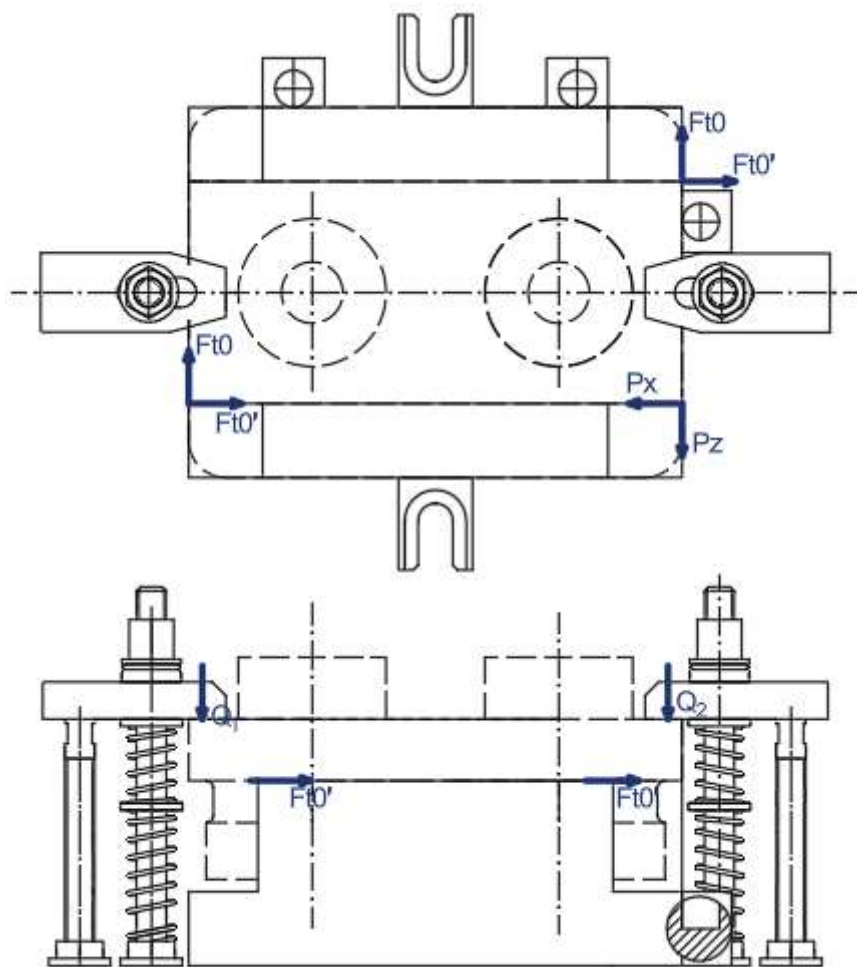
Розрахункова схема пристрою зі схемою сил, що діють на заготовку
